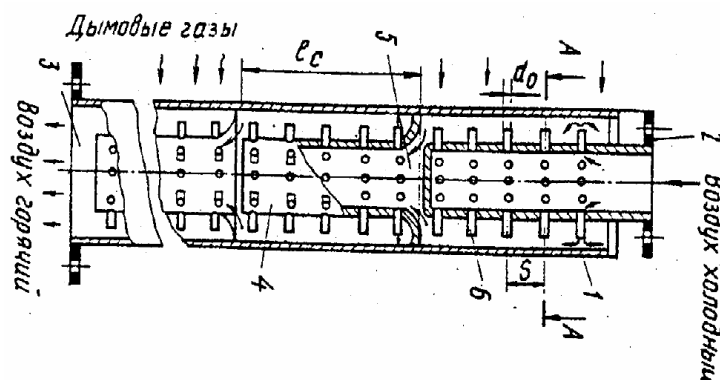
Струйный рекуператор [76]: 1 — корпус; 2 — патрубок подачи холодного воздуха; 3 — выходной патрубок нагретого воздуха; 4 — полая вставка; 5 — входной проем; 6 — газовыпускное отверстие с патрубком
